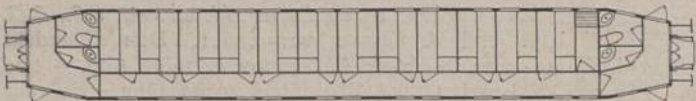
Grundriß eines Einheits-Schlafwagens 3. Klasse.
